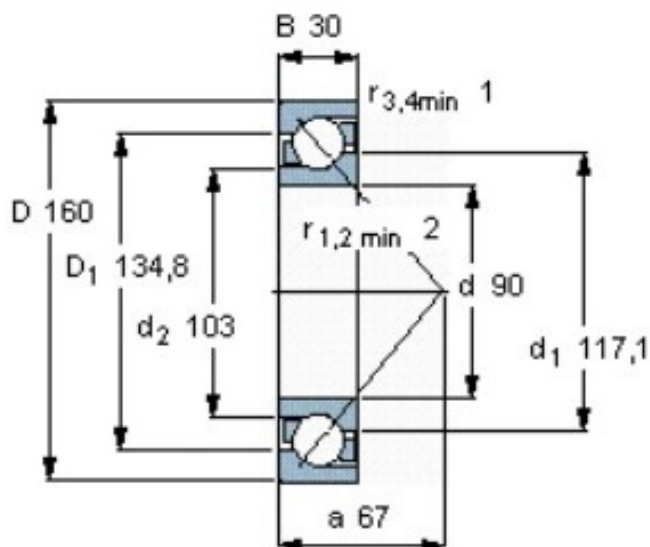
SKF 7220 BECBP EXPLORER [19]
